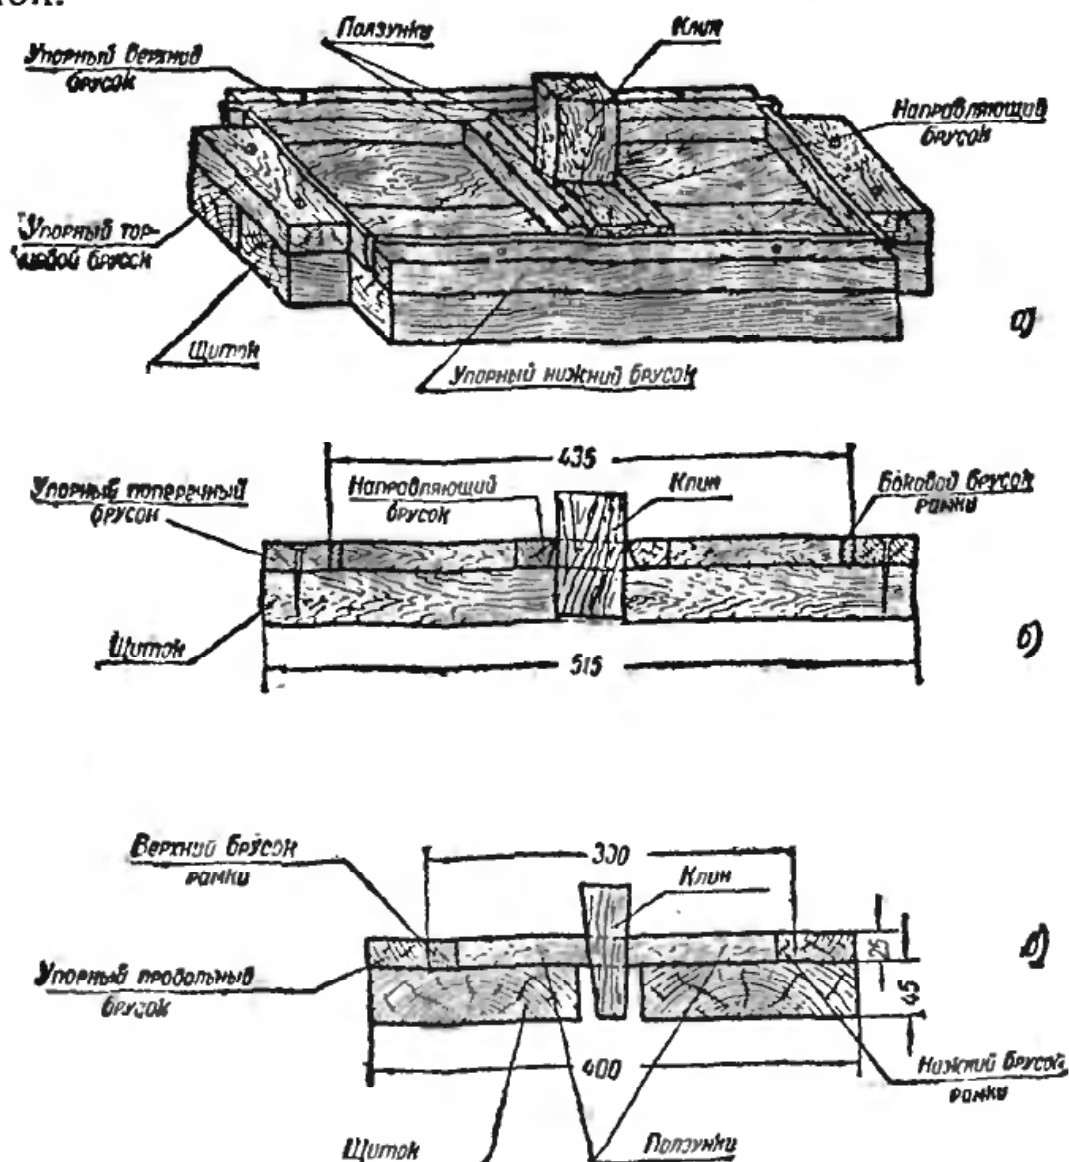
Шаблон для сборки рамок. а — общий вид шаблона с зажатой рамкой; б — продольный разрез шаблона; в — поперечный разрез.
